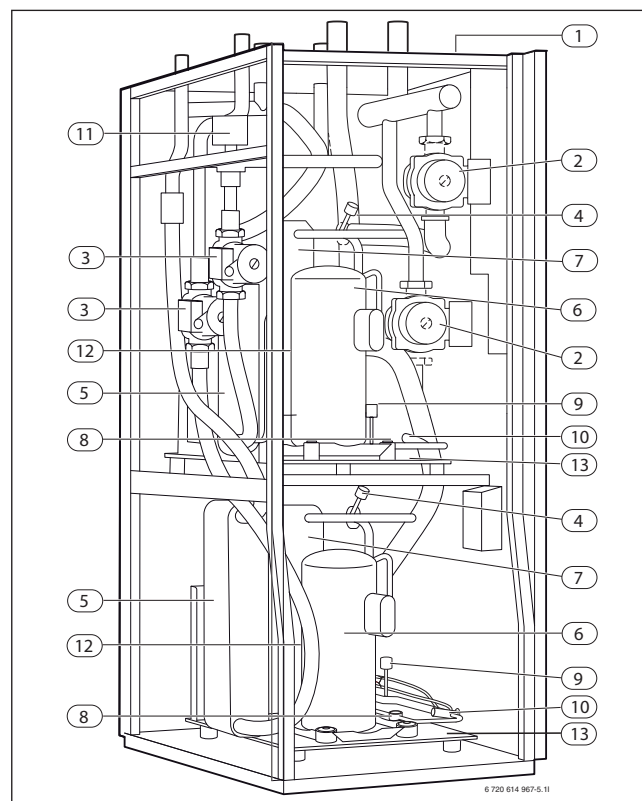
Ausgewählte Bauteile und Baugruppen der Wärmepumpe T 330-2
